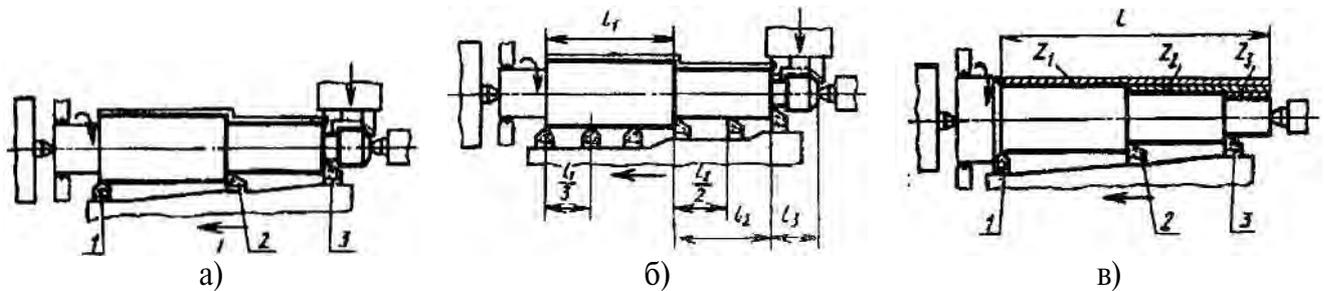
Схема обтачивания валков на станках с многолезцовыми головками
